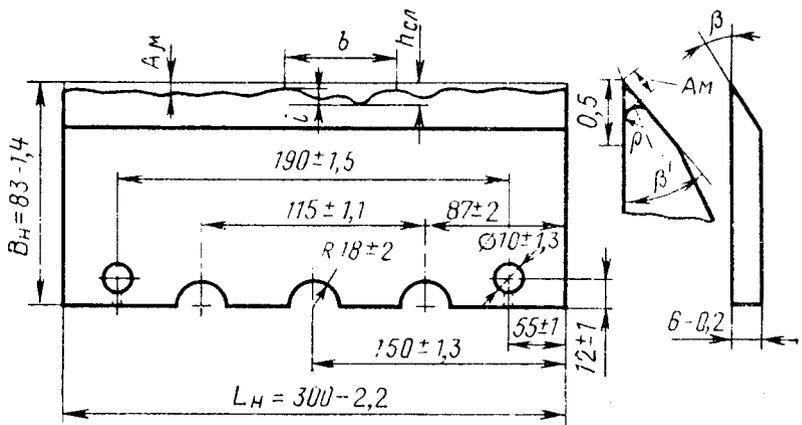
Основные размеры ножа, показатели износа и выкрашивания режущей кромки
